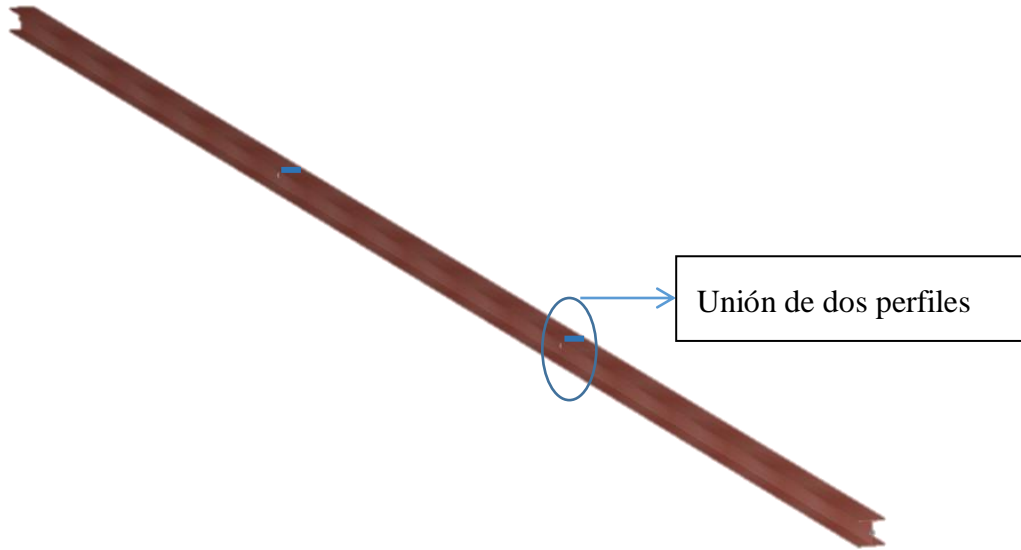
Reforzamiento longitudinal de una parte soldada.
